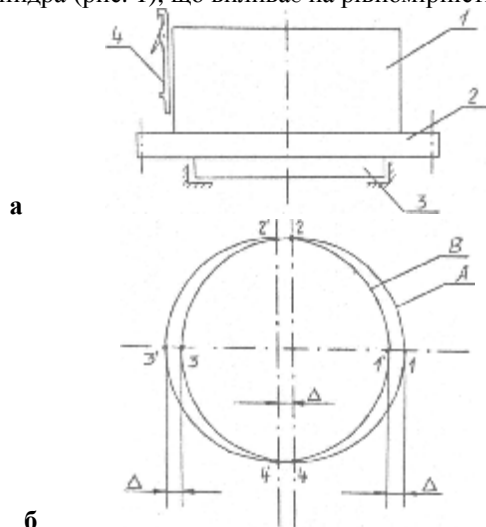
Опора голкового циліндра круглов'язальної машини типу КО: а – схема опори (1 – голковий циліндр; 2 – зубчасте колесо; 3 – опорна частина циліндра; 4 – голки); б – траєкторія руху голок (вигляд зверху): А – в початковий період роботи; В – при зношенні опори
